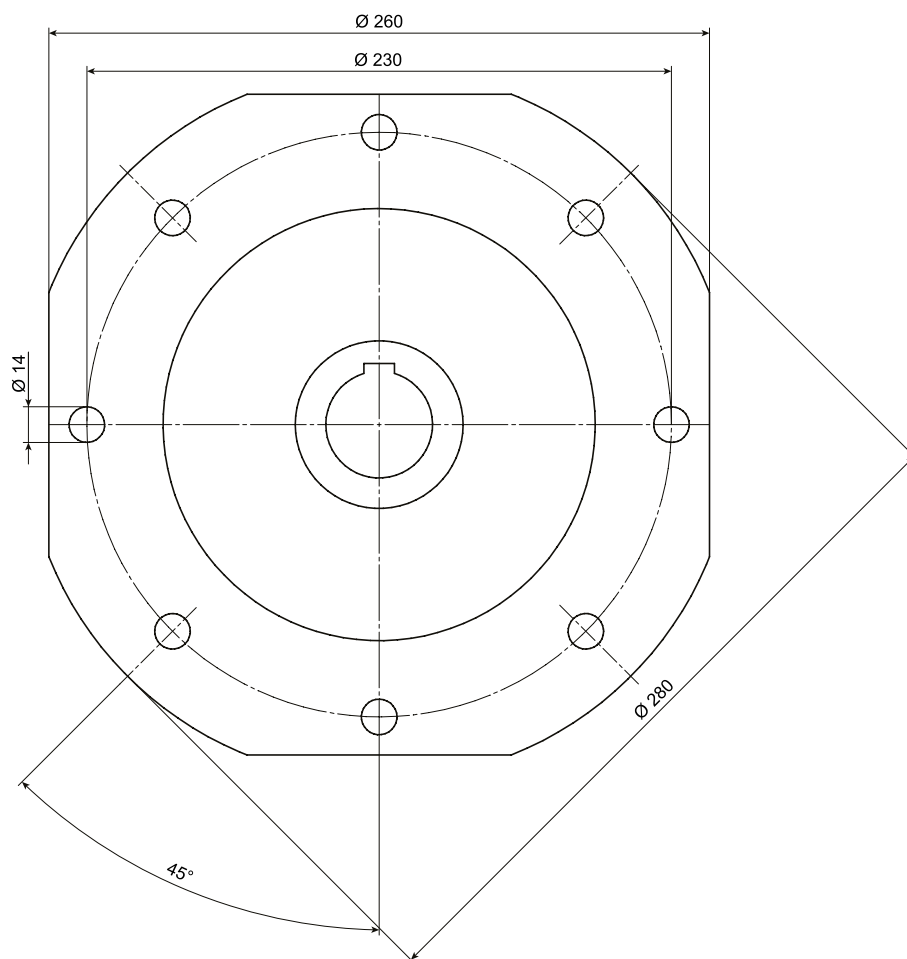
Габаритные размеры боковых фланцев FA и FB
